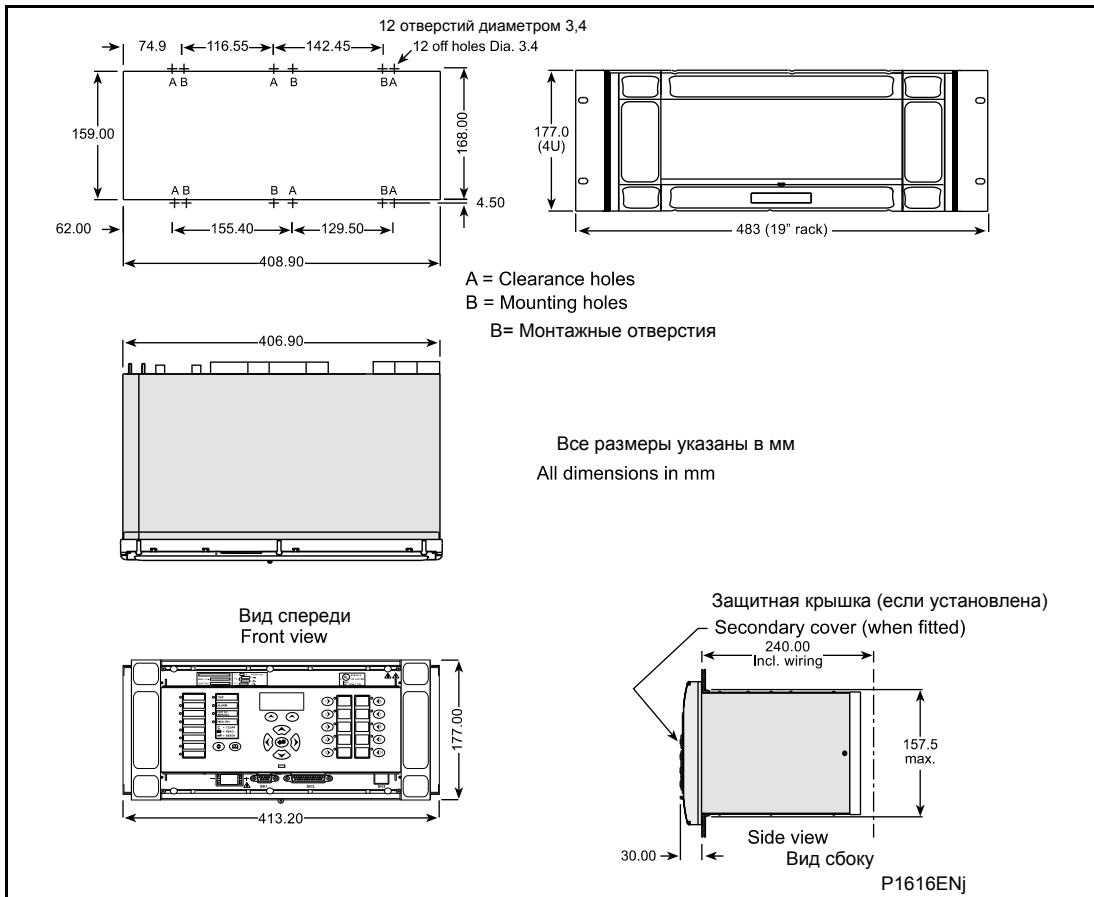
Размеры корпуса P243 (корпус 80TE)
